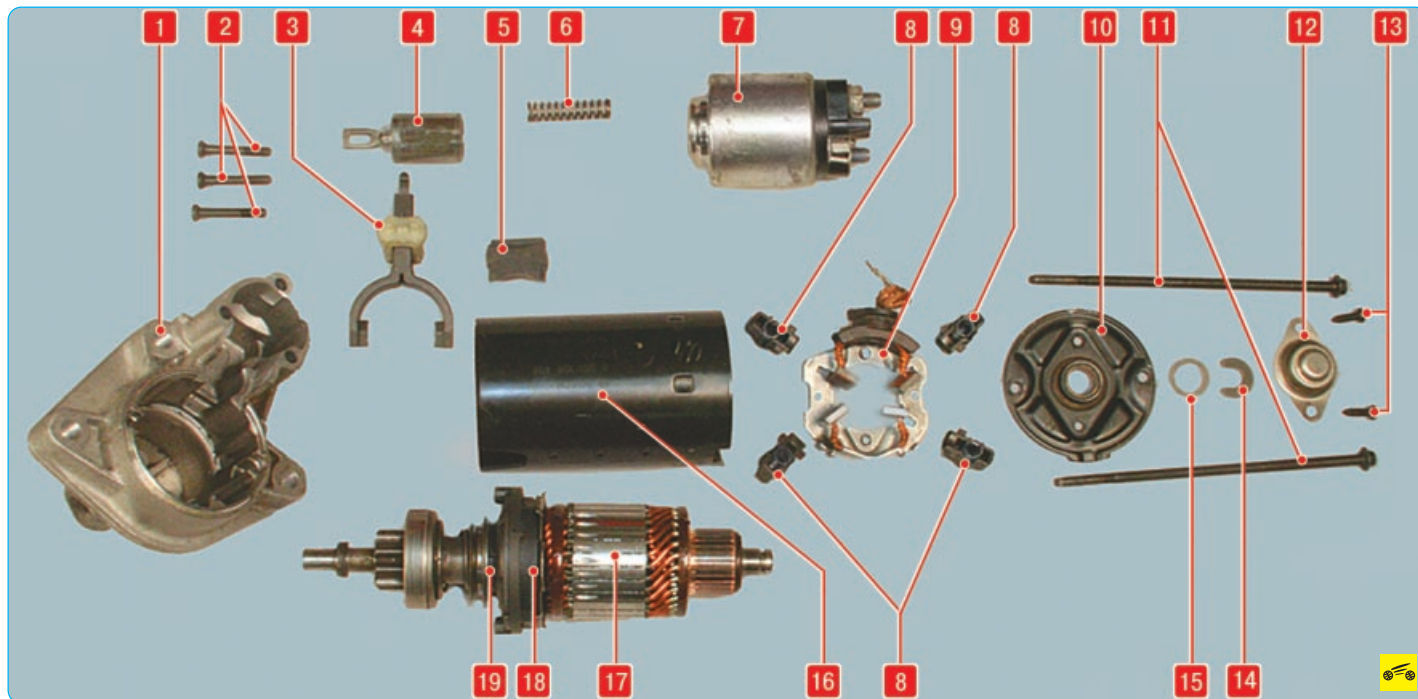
Детали стартера: 1 – крышка со стороны привода; 2, 13 – винты; 3 – рычаг привода; 4 – якорь реле; 5 – резиновый уплотнитель; 6 – возвратная пружина; 7 – корпус тягового реле; 8 – корпуса щеток в сборе с пружинами; 9 – щеткодержатель; 10 – крышка со стороны коллектора; 11 – стяжные болты; 12 – крышка подшипника; 14 – стопорная шайба; 15 – упорная шайба; 16 – корпус стартера; 17 – ротор стартера; 18 – планетарный редуктор; 19 – муфта свободного хода
